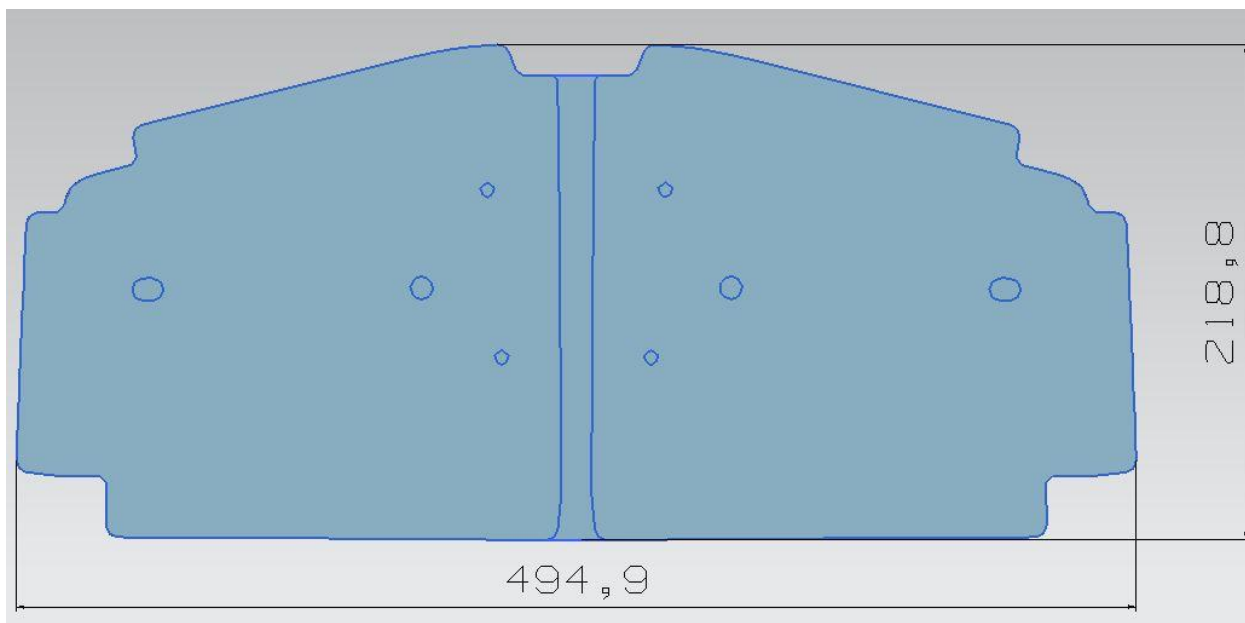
Развертка заготовки детали «Кронштейн крепления ремня безопасности»
